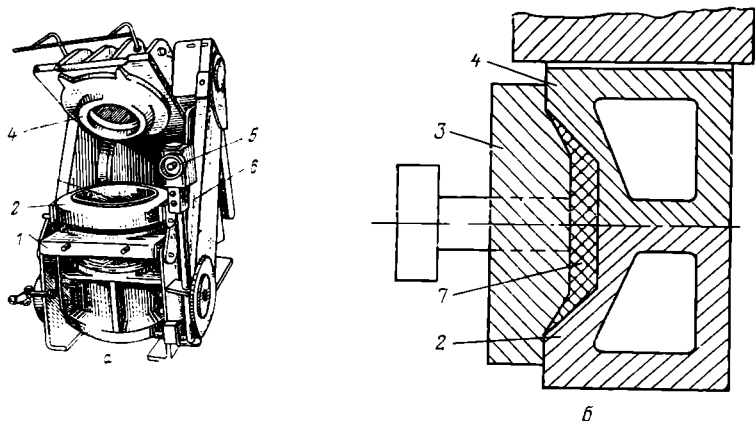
Вулканизатор механического действия для изготовления ободных лент:
